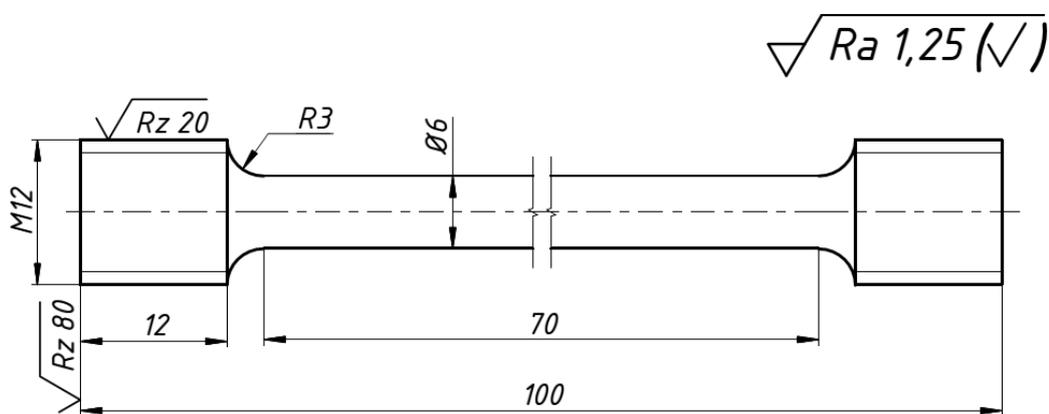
Стандартный пропорциональный цилиндрический образец по
